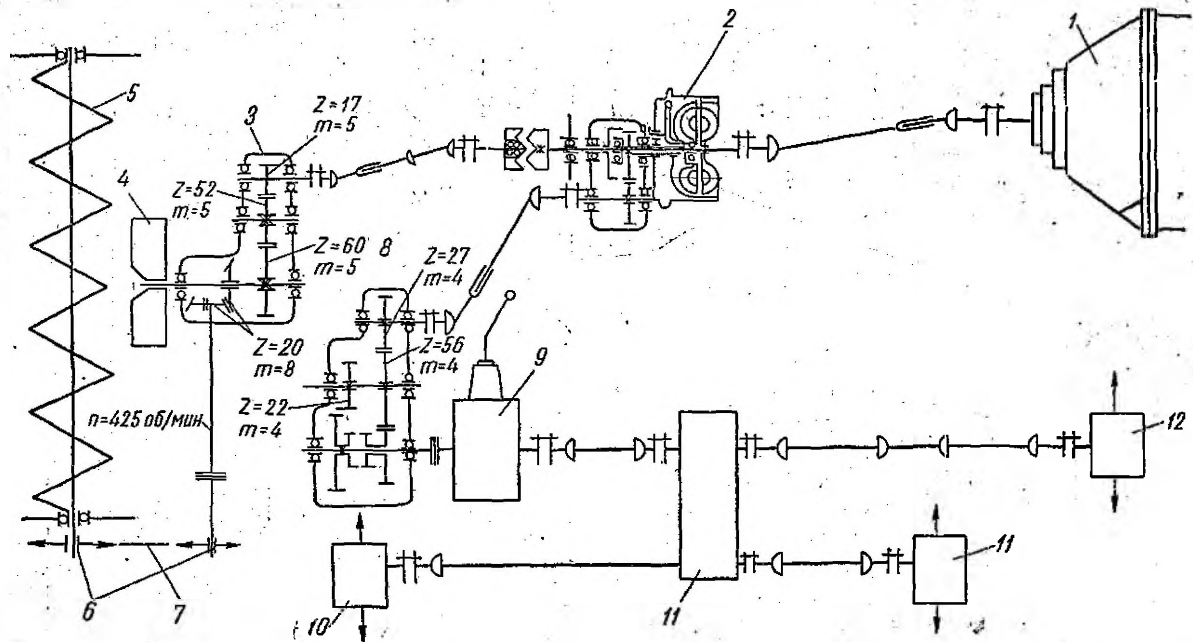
Кинематическая схема снегоочистителя Д-262: 1—двигатель; 2—турбосмуфта; 3—редуктор рабочей части; 4—роотор; 5—шнек; 6—звездочка; 7—цепь; 8—демультипликатор; 9—коробка скоростей; 10—главная передача переднего моста; 11—раздаточная коробка; 12—главная передача передней оси заднего моста; 13—главная передача задней оси заднего моста
